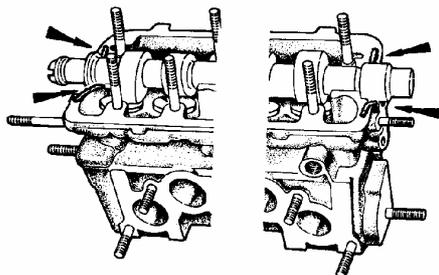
Нанесение уплотняющей прокладки на поверхность головки цилиндров двигателя ВАЗ-21114.
